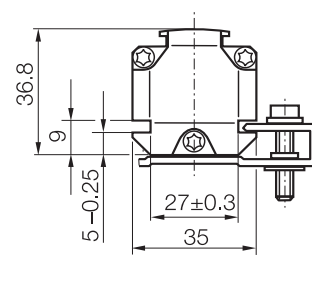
Rozměrový výkres (BTL5...P-S 86 odměřování s vedeným magnetem BTL5-F-2814-1S)
